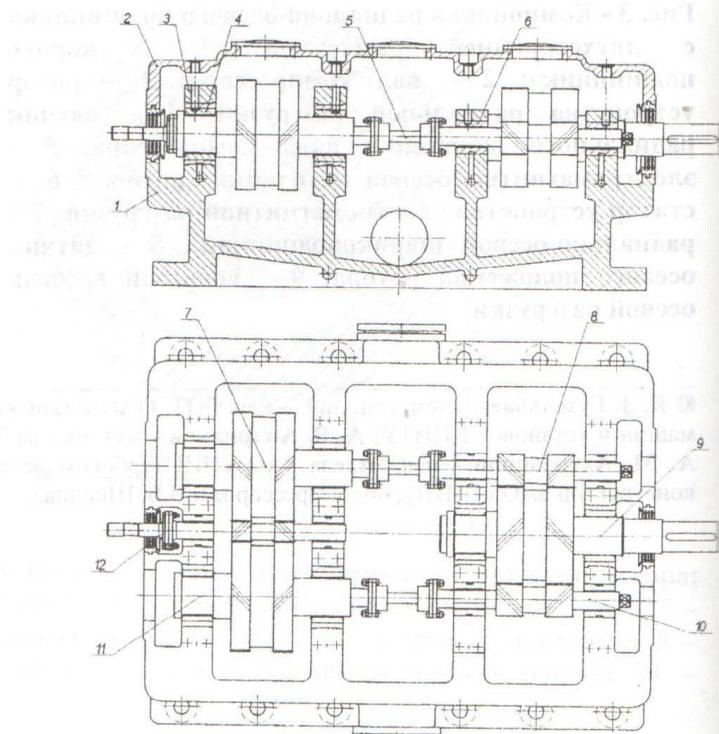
Двухступенчатый мультипликатор: 1 – корпус нижний; 2 – корпус верхний; 3 – крышка подшипника; 4 – вкладыш опорно-упорный; 5 – муфта зубчатая; 6 – вкладыш опорный; 7, 9, 11 – колесо зубчатое; 8, 10, 12 – вал-шестерня
